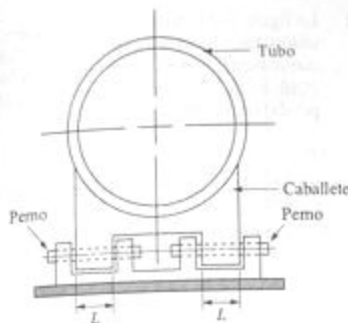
Caballete para el tubo del problema 3-33.
